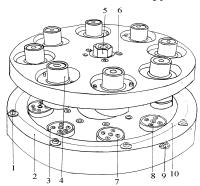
Закаточный механизм машины КАН-О-МАТ: 1 — крепежный болт для клинчера; 2 — клинчер; 3 — закаточная тарелка; 4 — патрон прижимной; 5 — гайка для регулирования диска по высоте; 6 — крепежный болт для диска; 7 — крепежный болт для закаточной тарелки; 8 — болт для крепления подшипника; 9 — болт для крепления клинчера к зубчатому венцу; 10 — клинчер
